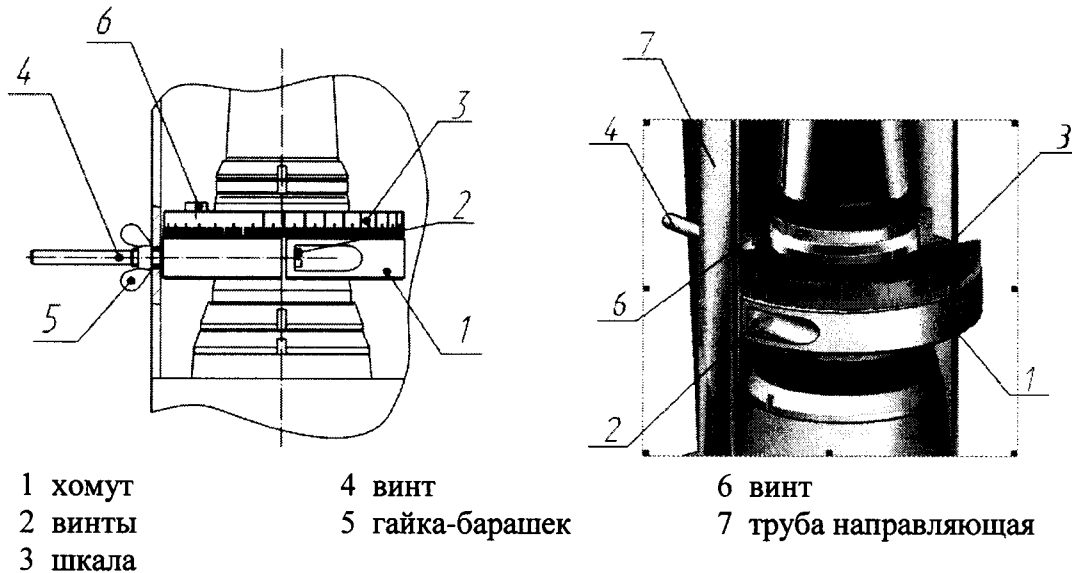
Установка приспособления для ручного поворота ЗТ-ГК
